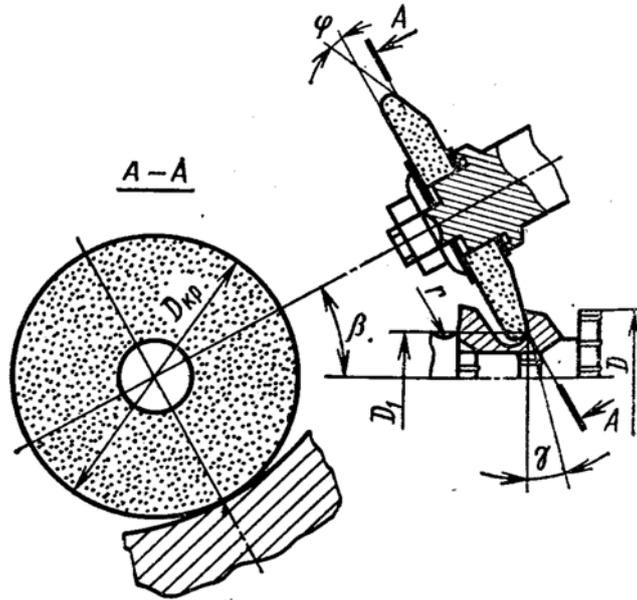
Схема заточки зуба круглой протяжки по передней поверхности
